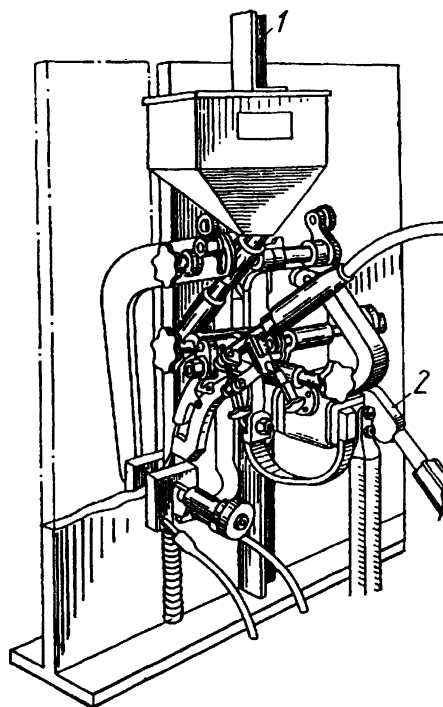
Сварочный полуавтомат А820МК
